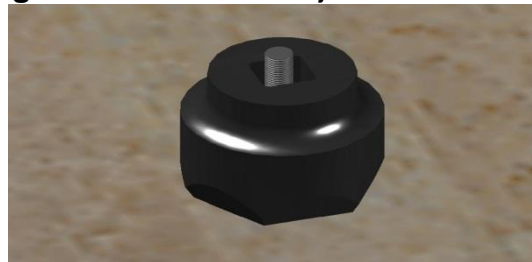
Ensamblaje Componentes Internos del Troquel
